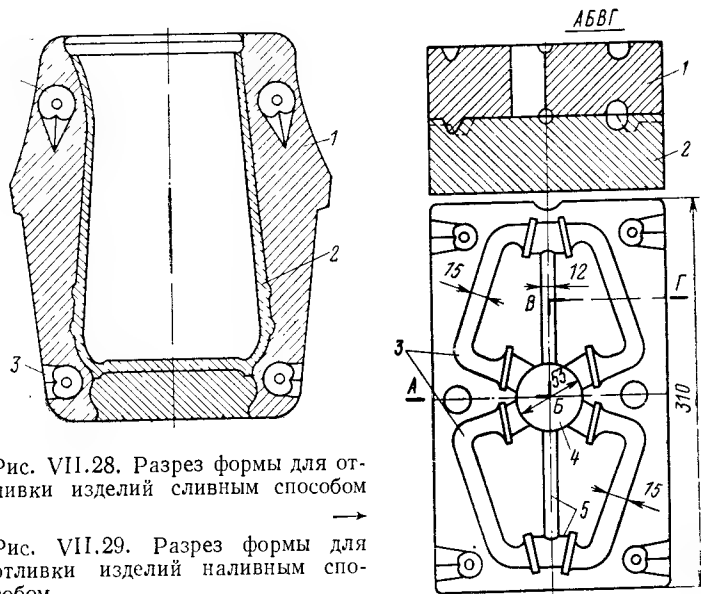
Разрез формы для отливки изделий сливным способом
